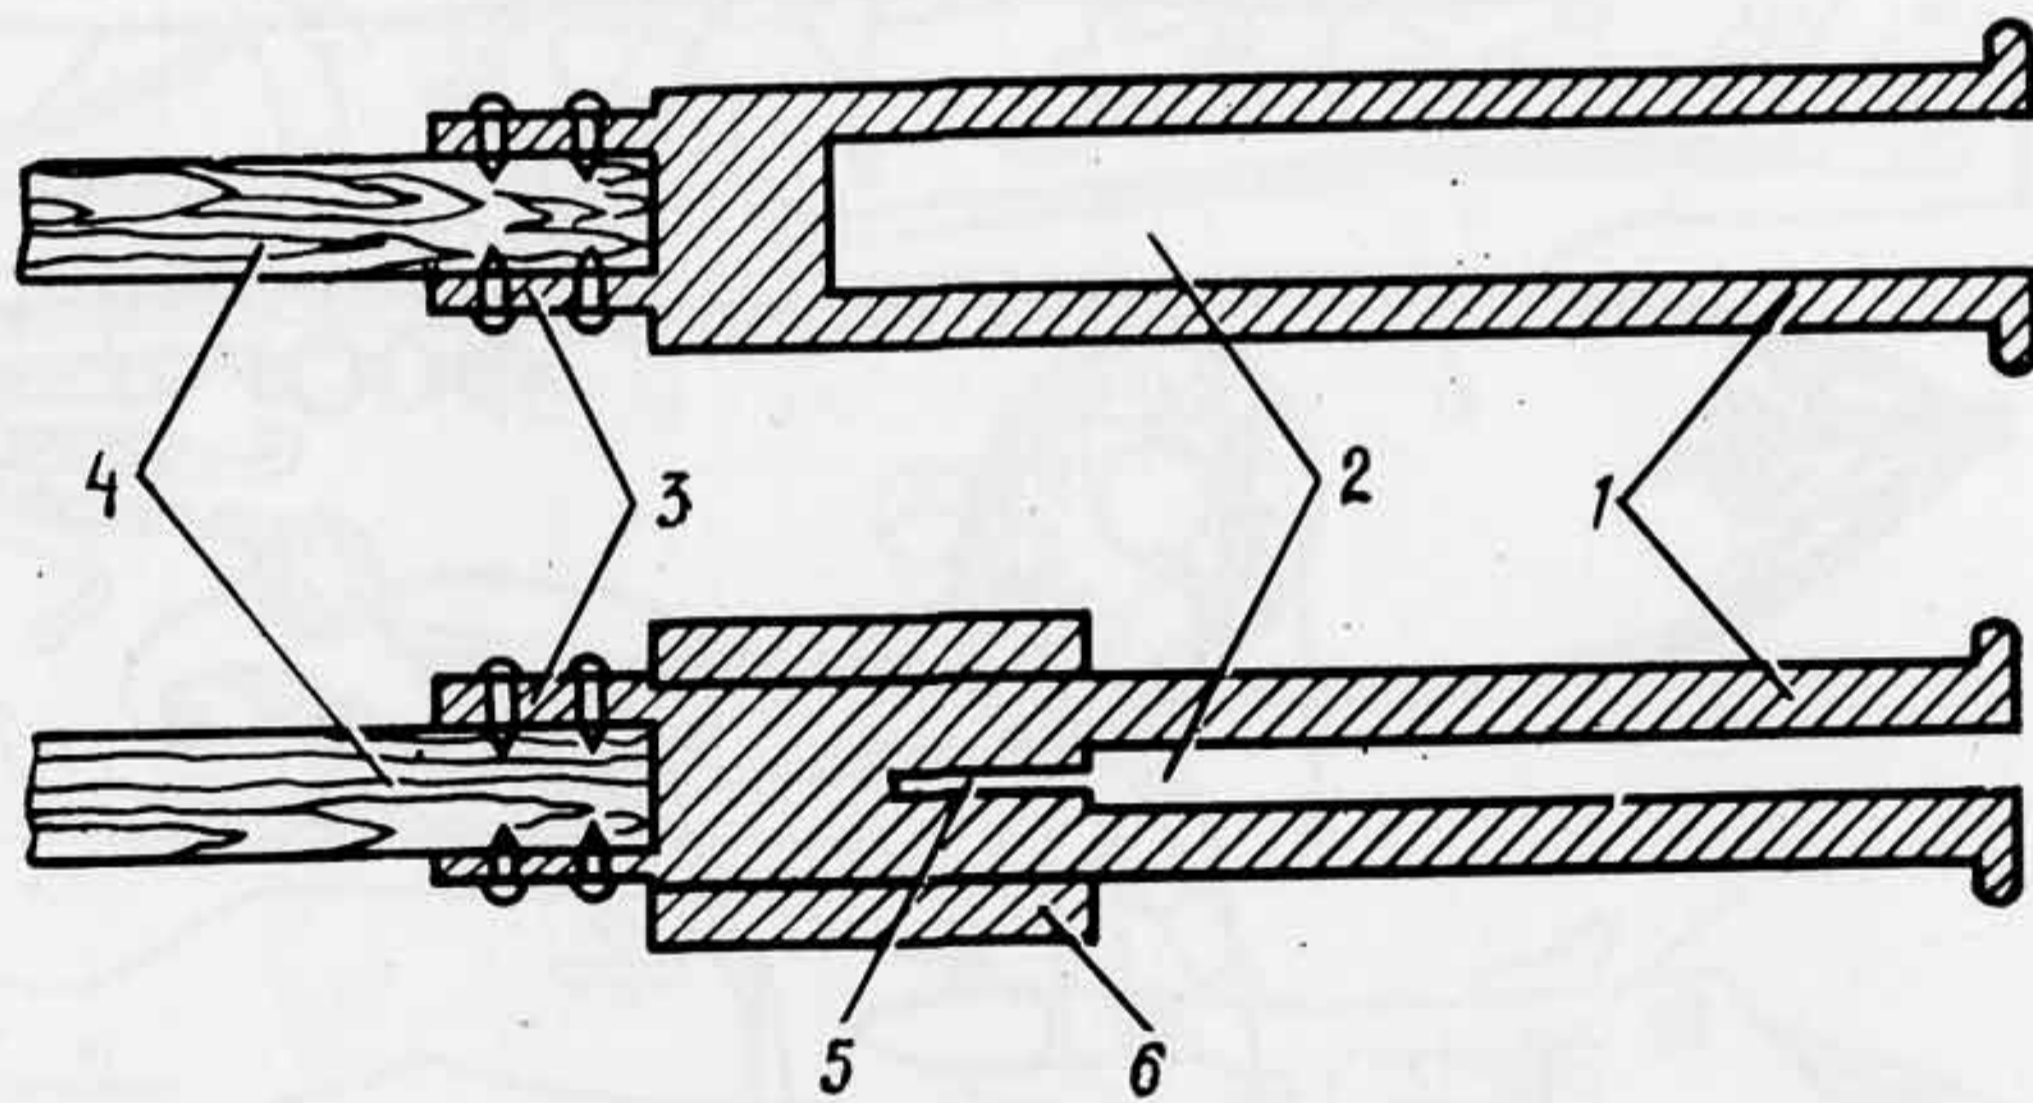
Схематический чертеж ручной пищали конца XIV — начала XV в. (вид сверху):
